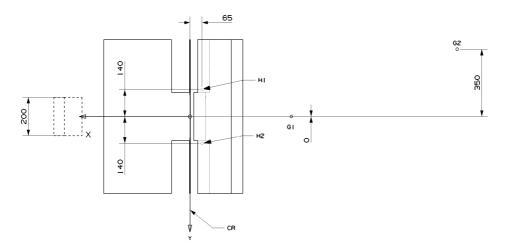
Вид сбоку – Стенд с креплениями (общий допуск: ±2)
